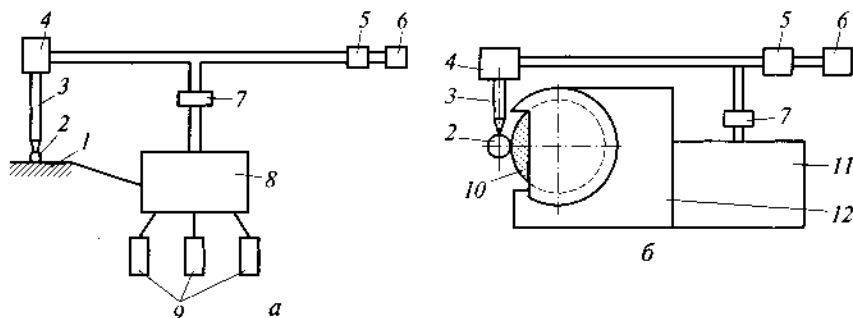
Схемы автоматов пассивного (а) и активного (б) контроля: 1 — измерительное приспособление; 2 — деталь; 3 — шток; 4 — размерный датчик; 5 — счетчик; 6 — сигнализация; 7 — промежуточное звено; 8 — сортировочное устройство; 9 — ящик для рассортирования деталей; 10 — инструмент; 11 — исполнительный механизм; 12 — шлифовальная бабка
